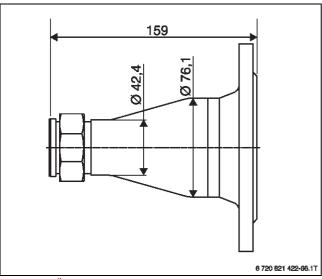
Übergangsstück DN 65/PN 6 – G 1 ½ " (Maße in mm)
